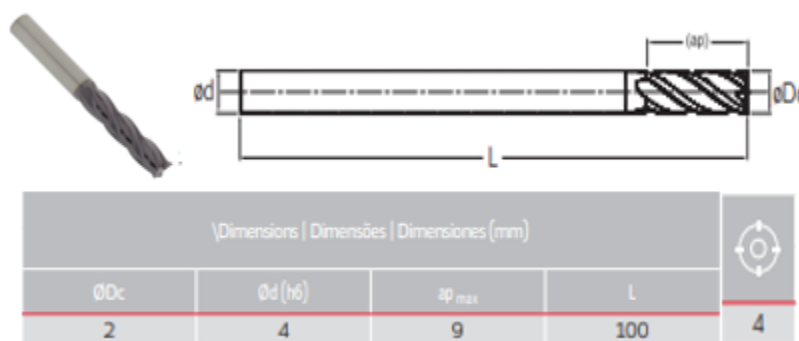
Fresa plana de diámetro 2 mm. Fuente [9]
